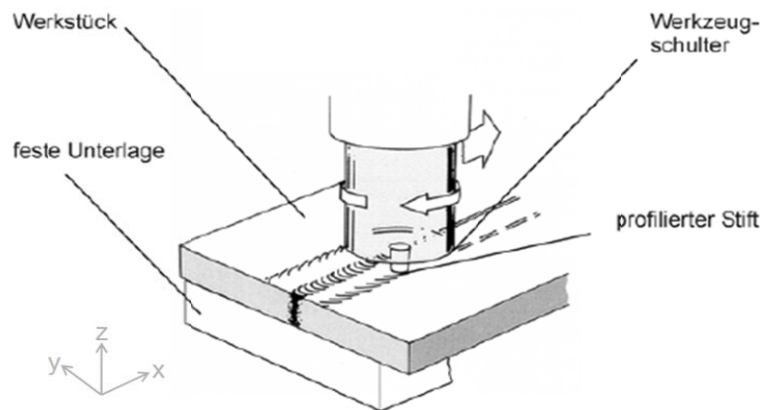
Verfahrensprinzip Friction Stir Welding [9 S. 131]
